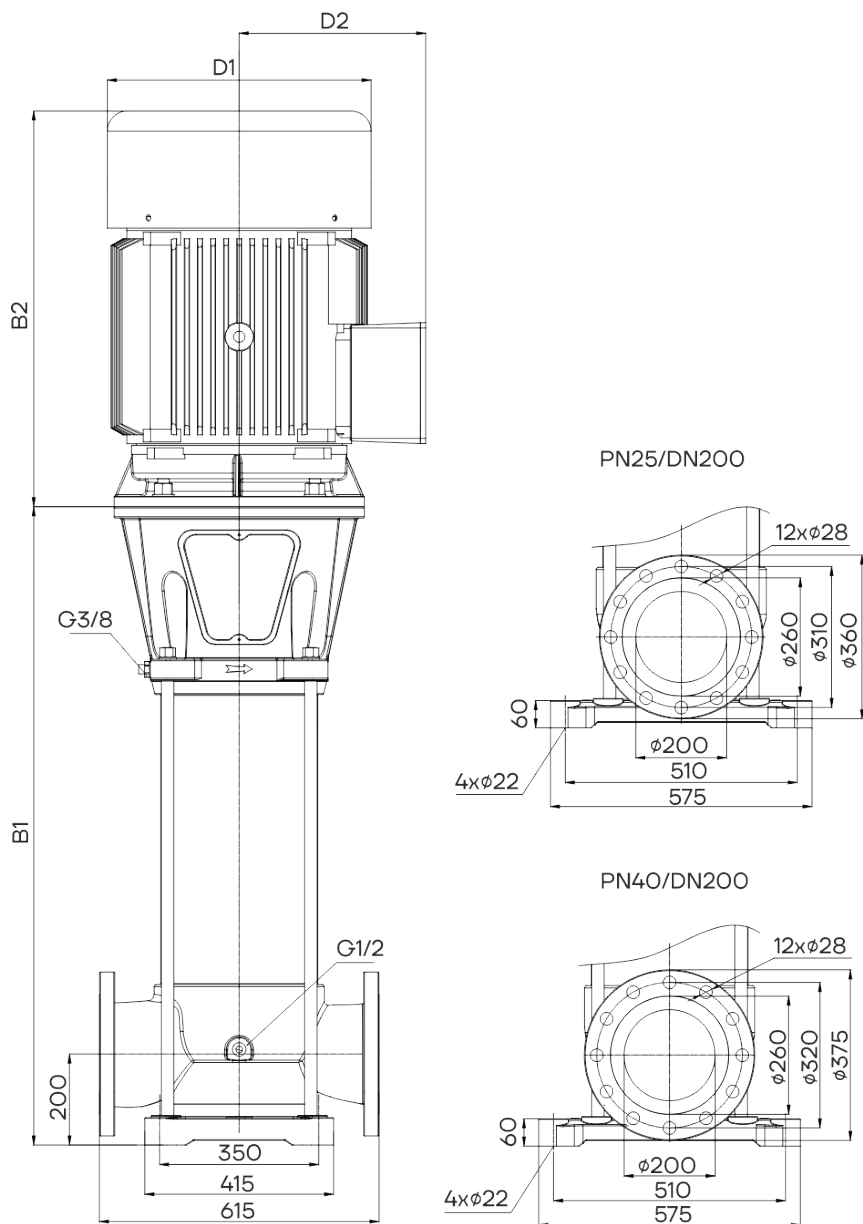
М Габаритно-присоединительные размеры VMB(F)-H 190, 220, 260
